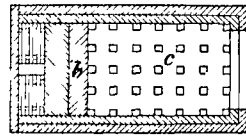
Four à cuire les tubes; coupe horizontale.
